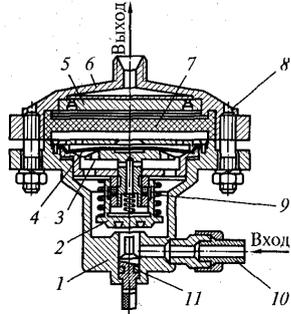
Схема затвора сухого типа ЗСЗ – 1: 1 – корпус; 2 – клапан; 3 – шток; 4 – мембрана; 5 – отбойник; 6 – крышка; 7 – пламегасящий элемент; 8 – шпильки; 9 – пружина; 10 – нипсель; 11 – шток.
